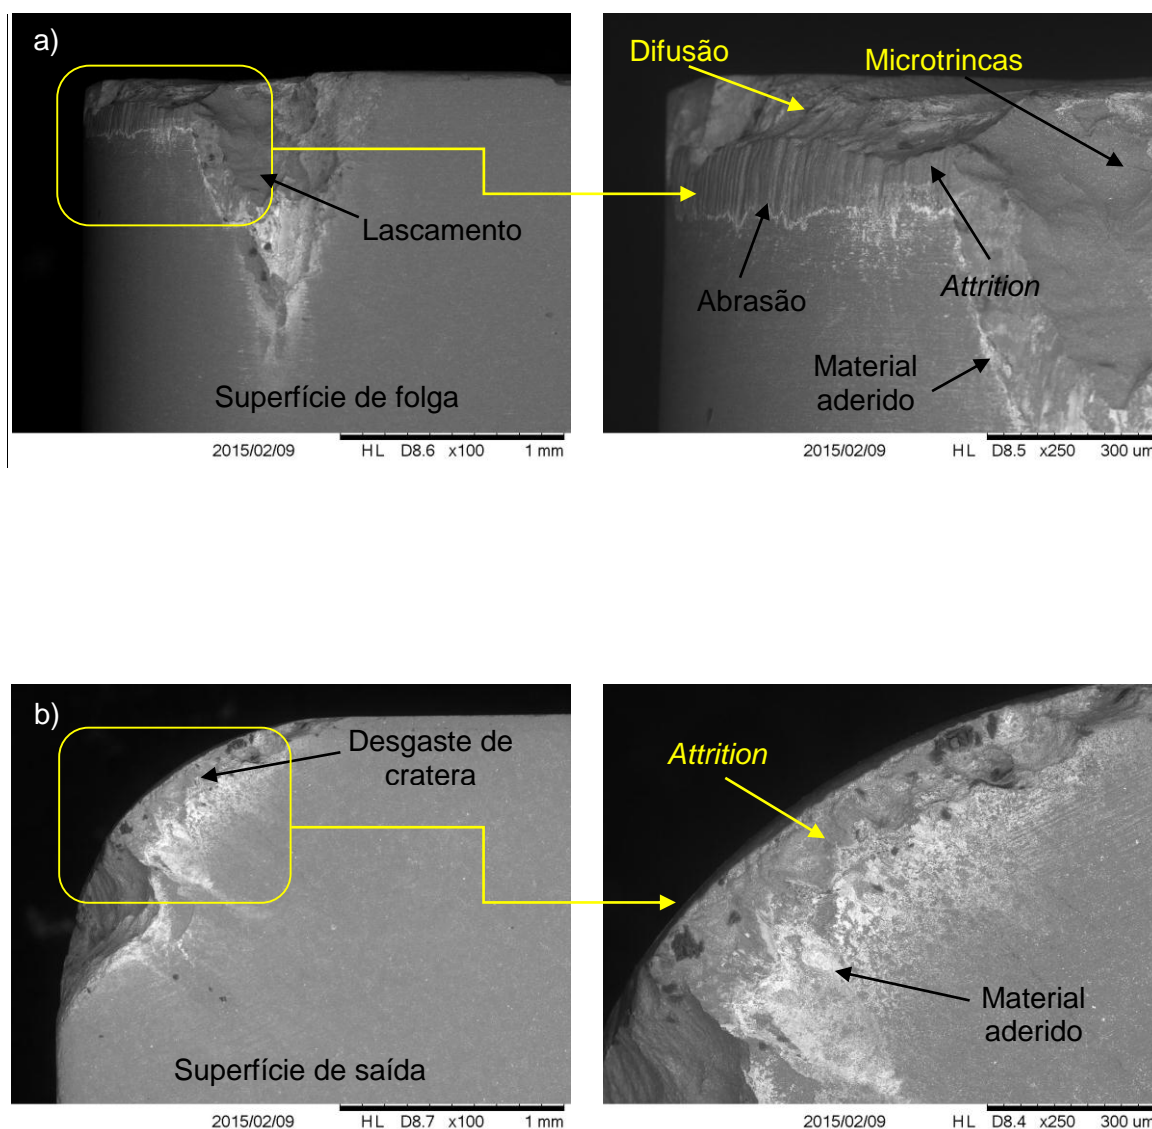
Fotografias obtidas através do MEV das ferramentas *whisker* após a usinagem do Inconel 718 com aplicação de fluido de corte LB 2000 + 20% MoS₂ por MQF. (a) superfície de folga e (b) superfície de saída
